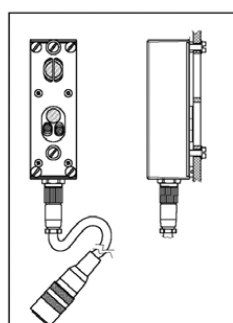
Sensore con cavo innestabile. Sensor with cable engaged.
